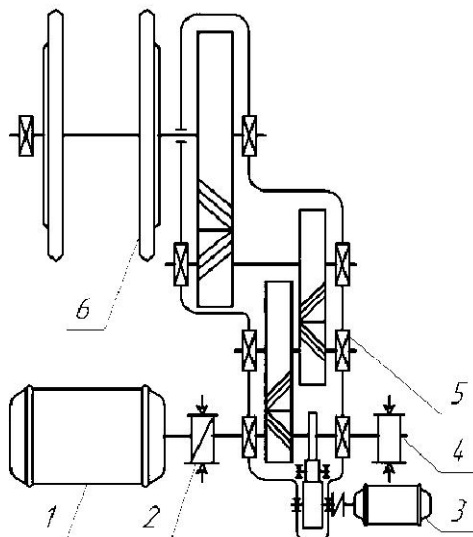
Схема ПГТЭ Е55Т, Е-75Т / ЭС-02, ЭС-03: 1 – главный электродвигатель; 2 – рабочий тормоз и тормозная муфта; 3 – вспомогательный электродвигатель с редуктором; 4 – второй рабочий тормоз с тормозным шкивом; 5 – редуктор; 6 – главный вал с тяговыми звездочками и аварийным тормозом
